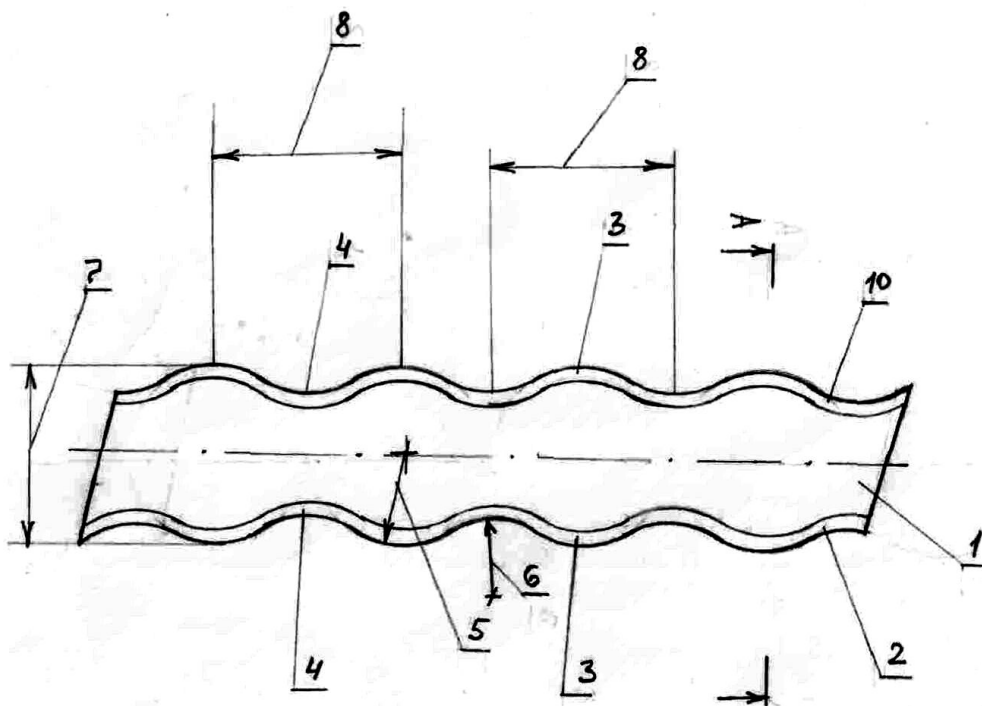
Двухсторонний зубчатый нож плоскорезной лапы.
